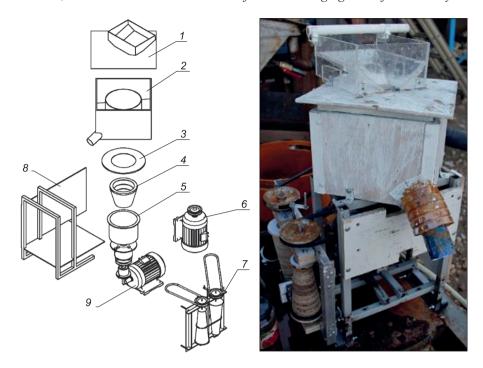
Общий вид лабораторной модели центробежно-вибрационного концентратора. I — крышка с приемным бункером, 2 — кожух, 3 — зажимное кольцо, 4 — съемная футеровка, 5 — узел рабочего органа, 6 — приводной двигатель, 7 — валковый вариатор, 8 — несущая рама, 9 — двигатель вибратора.
